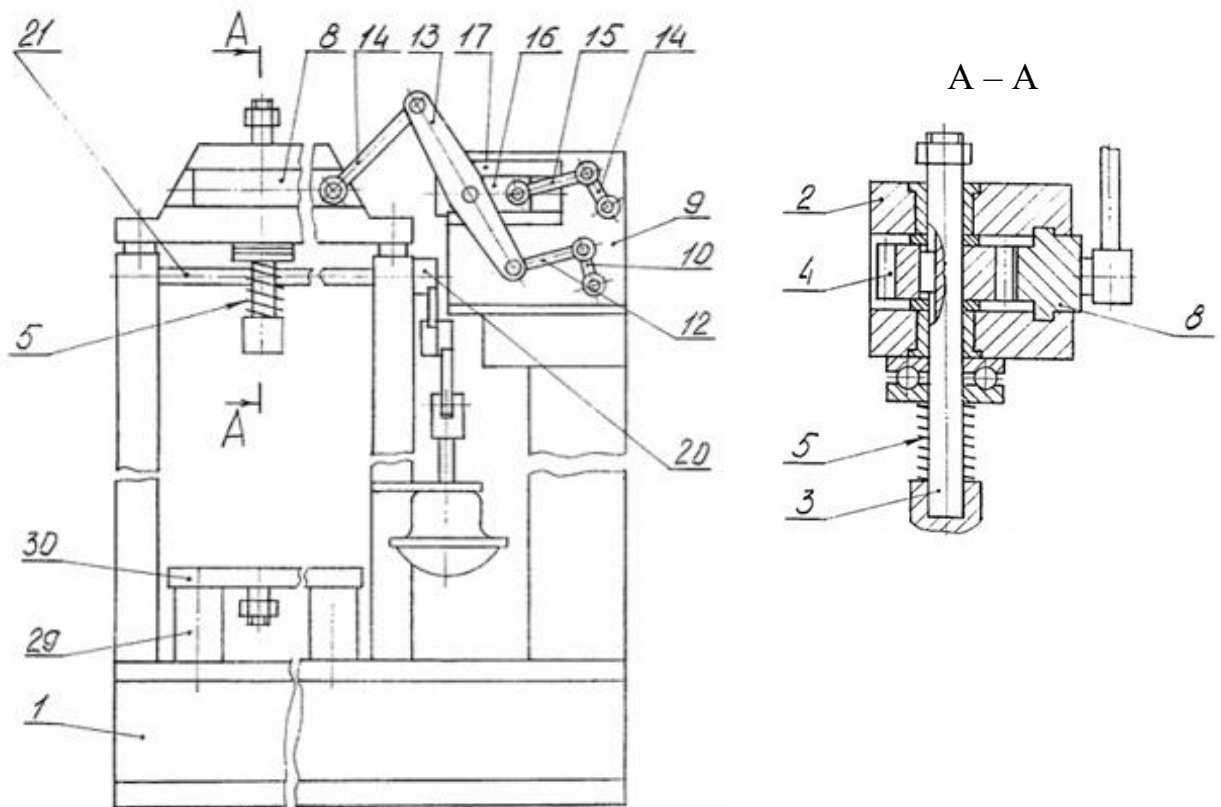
Вид А лабораторної установки для дослідження працездатності притирального складу: 1 – станина; 2 – корпус; 3 – шпindelь; 4 – шестерня; 5 – пружина; 8 – рейка; 13 – важіль; 16 – повзун; 17 – напрямні; 20 – важель; 21 – вал; 29 – рейка; 30 – плита
